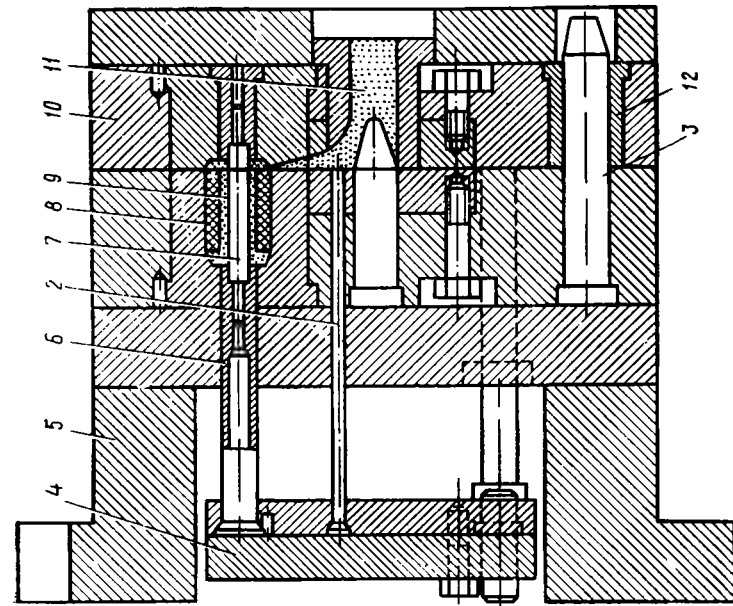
Четырехместная пресс-форма для крепления вала и сердечника заливкой алюминия:
